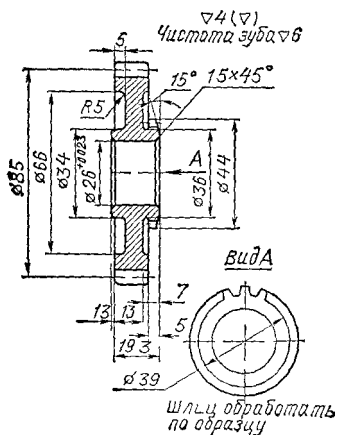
Шестерня второй передачи вторичного вала спортивной коробки
